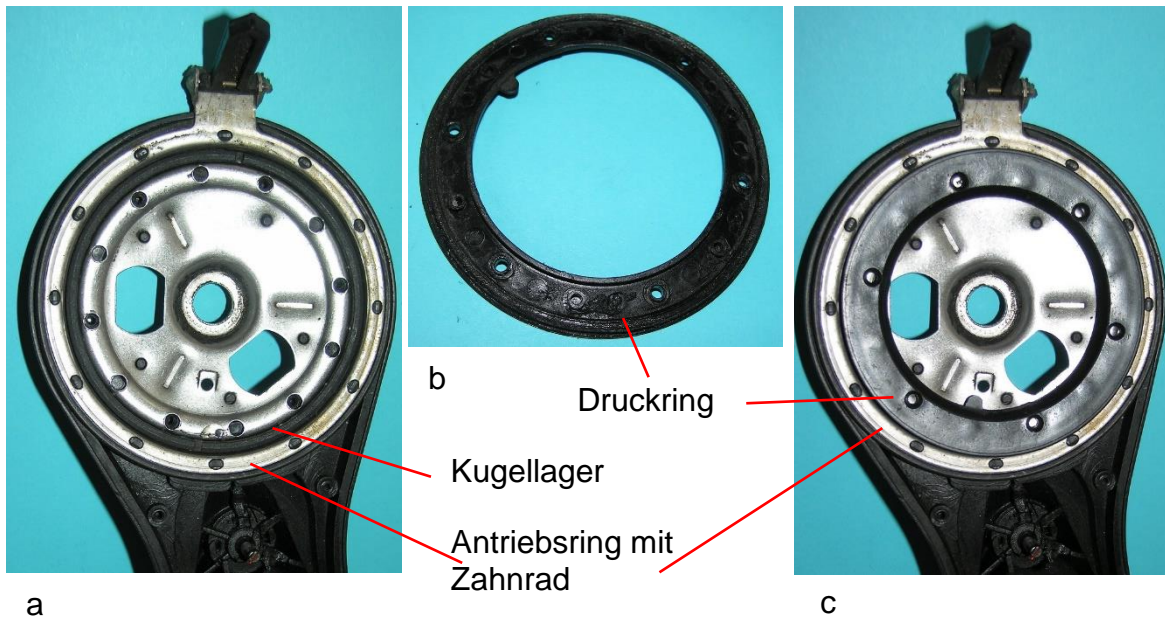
Montage des Druckrings: a) Antriebsring und Kugellager eingelegt, b) Druckring, c) Montierter Druckring
